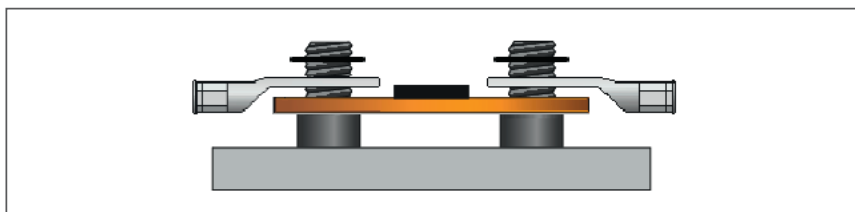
Leitungen HV-, Ringkabelschuhe und Unterlegscheiben auf Gewindebolzen aufsetzen
